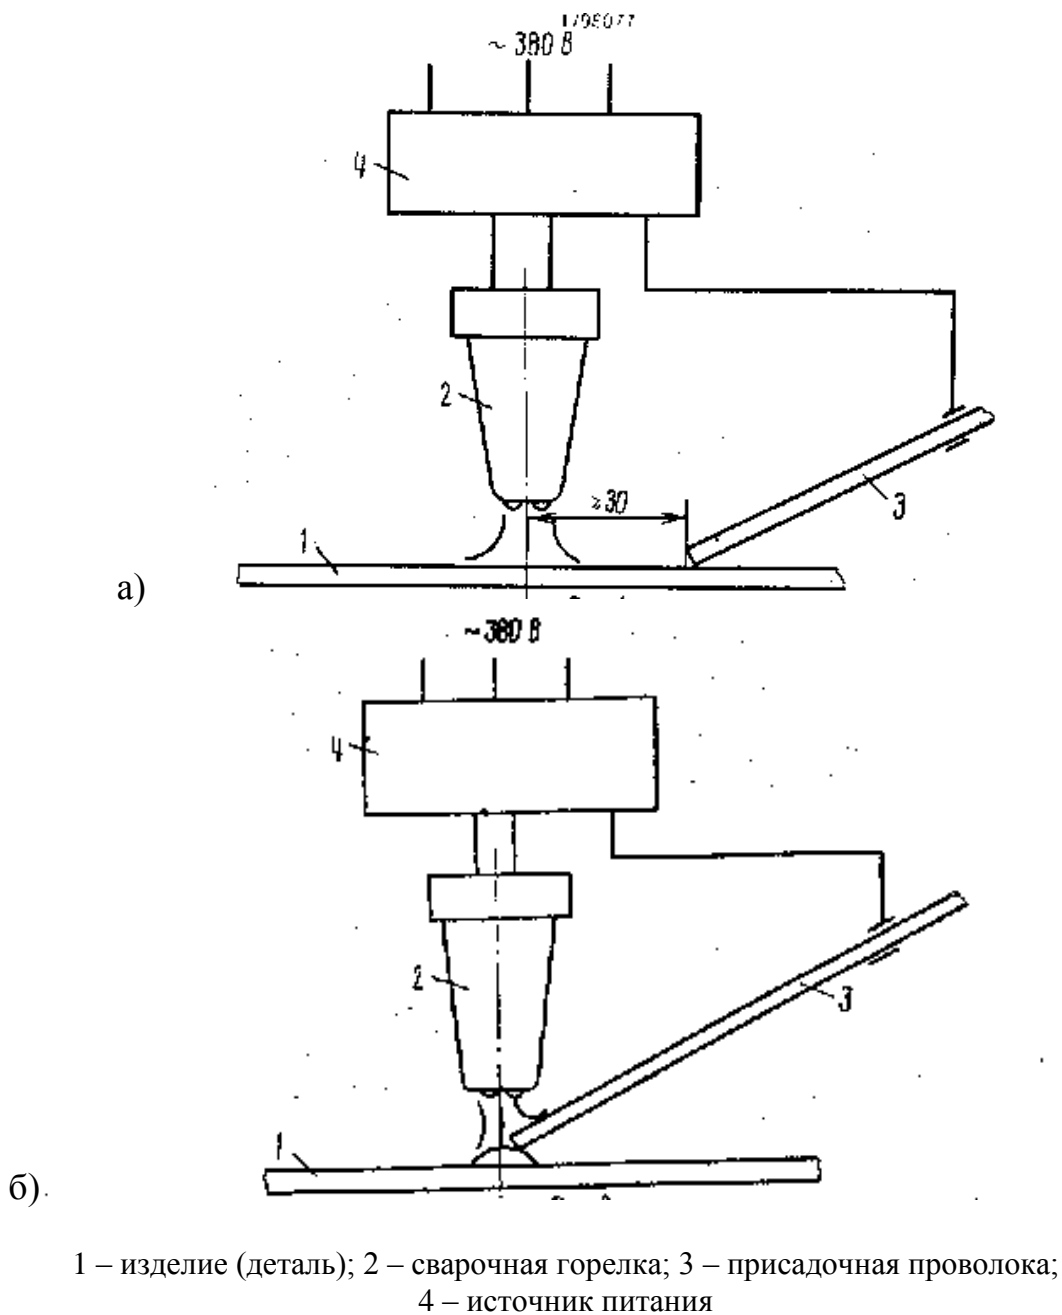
Осуществление ремонтной сварки трёхфазной дугой: замыкания конца присадочной проволоки на изделие (а) и перенос конца присадочной проволоки в сварочную ванну (б)
